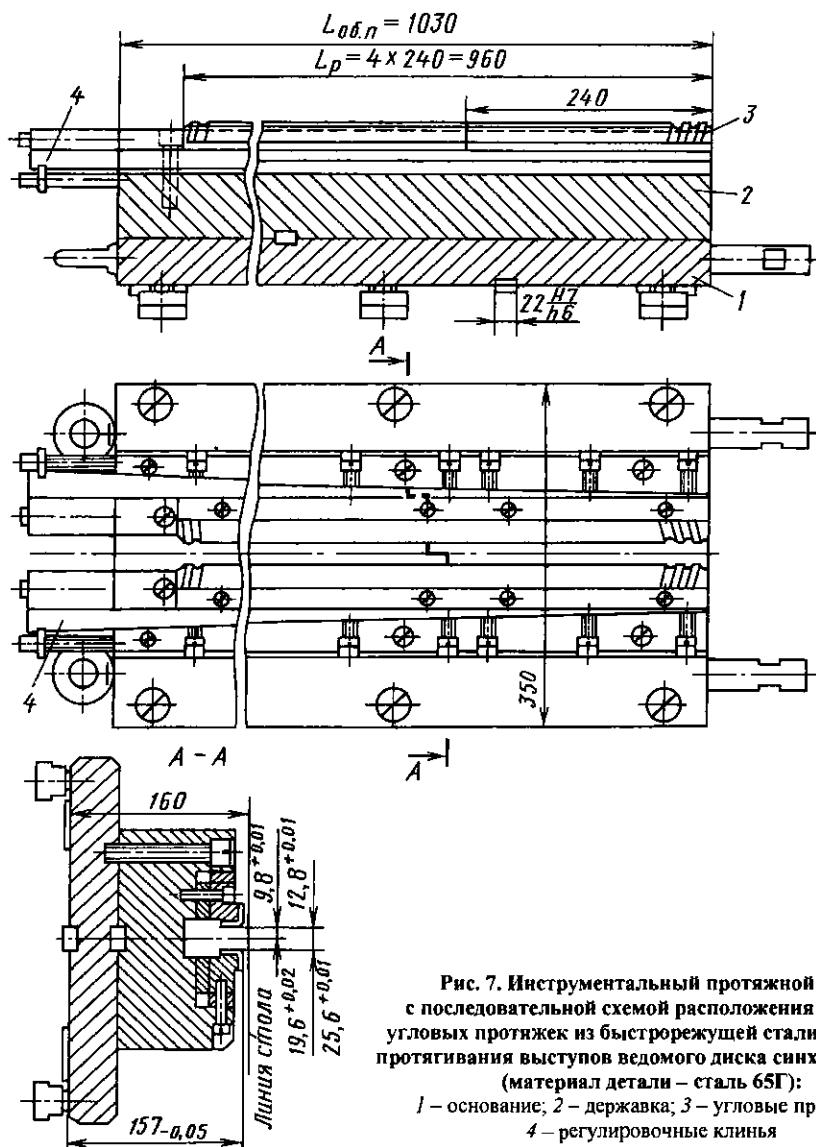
Инструментальный протяжной блок с последовательной схемой расположения плоских угловых протяжек из быстрорежущей стали Р6М5 для протягивания выступов ведомого диска синхронизатора (материал детали – сталь 65Г):
